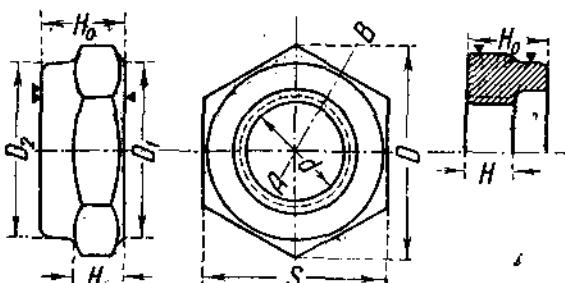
Гайка отжимная шестигранная для упорных центров с мелкой метрической резьбой.
